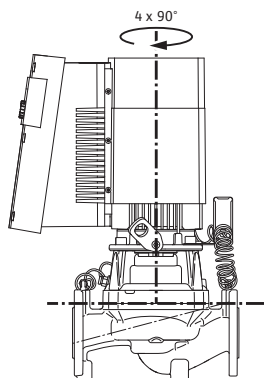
Přípustné polohy instalace se svislým hřídelem motoru
